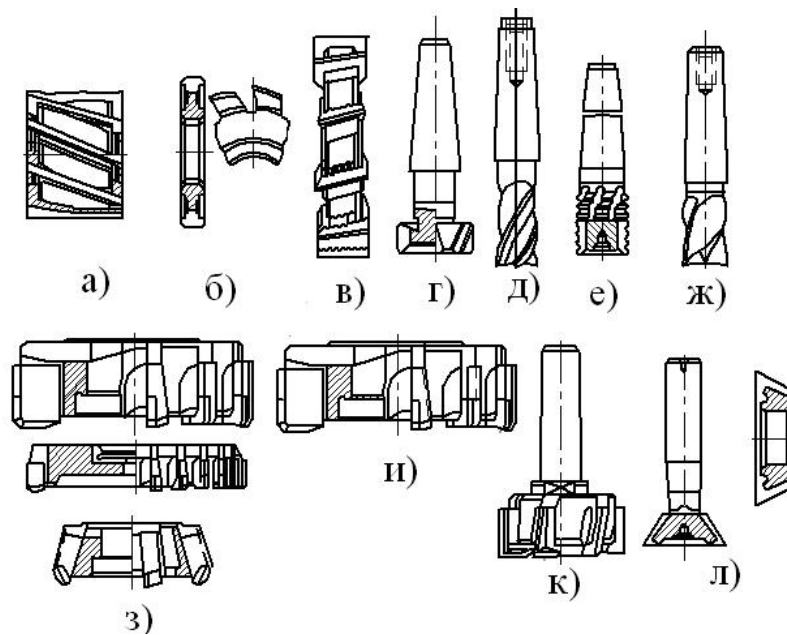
Основні типи фрез: а – циліндрична; б, в – дискова; г - Т-подібна; д – кінцева; е – кінцева обдирна; ж – шпонкова; з - торцева насадна; и - торцева східчаста; к - торцева з хвостовиком; л – кутова
